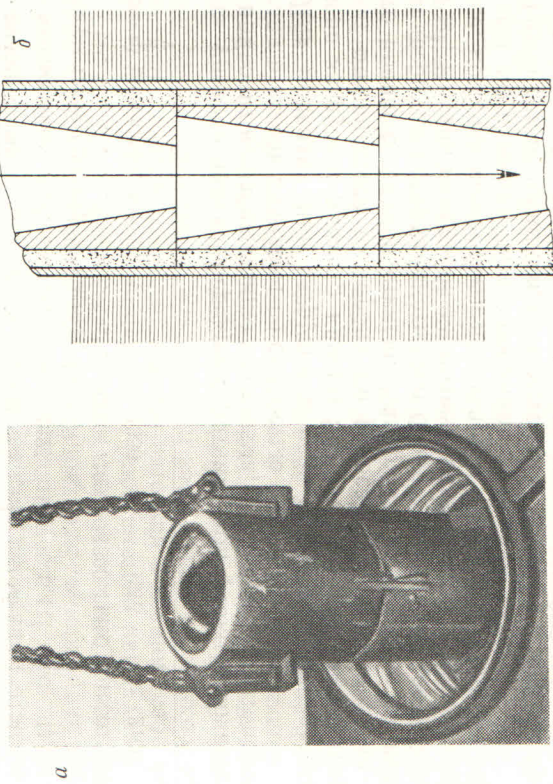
Труба для заливки жидкого металла в тигель печи:
